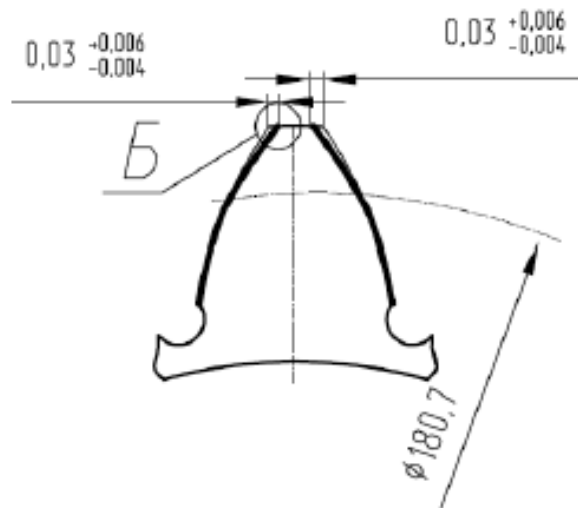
Модифікації профілю зуба циліндричного зубчастого колеса
